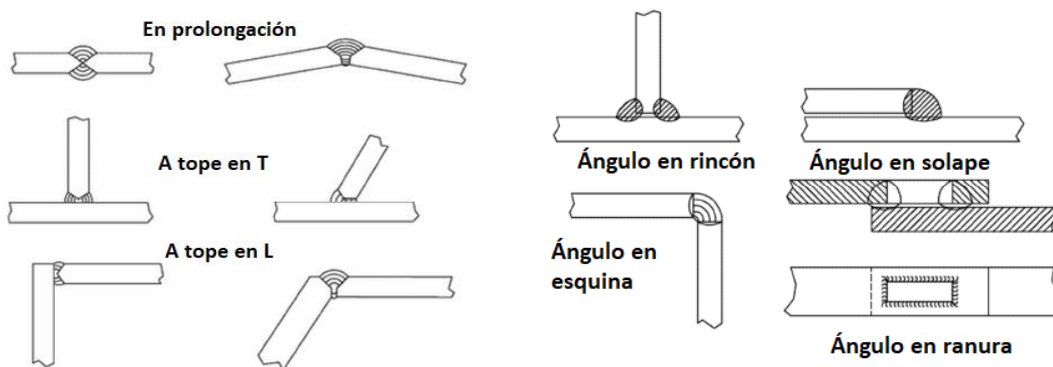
Uniones soldadas a tope (izquierda) en ángulo (derecha). [18]
